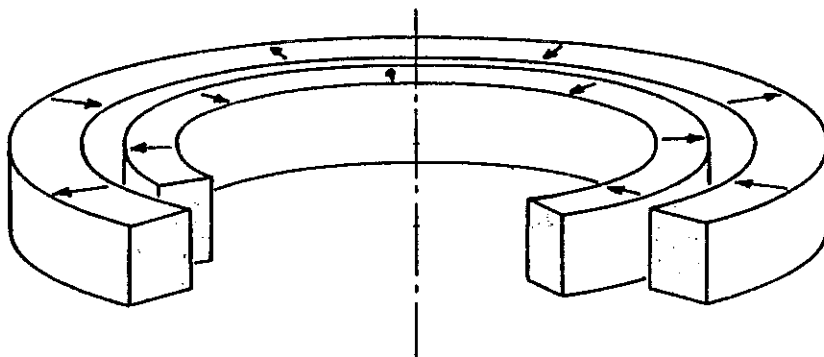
Vue éclatée d'un coupleur coaxial
